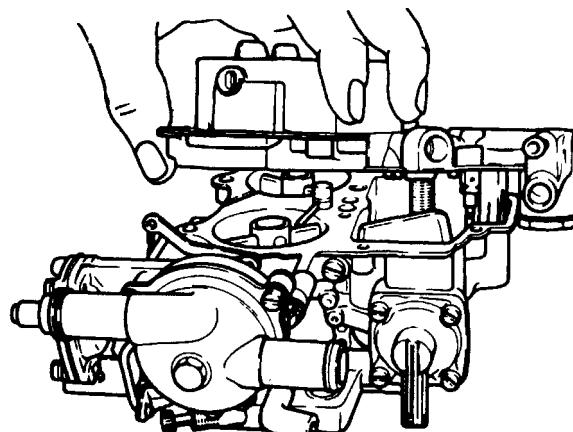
Снятие верхней части корпуса карбюратора - карбюратор WEBER.
